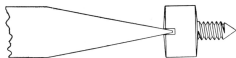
Schraubenzieher im Einschnitt der Schraube.
